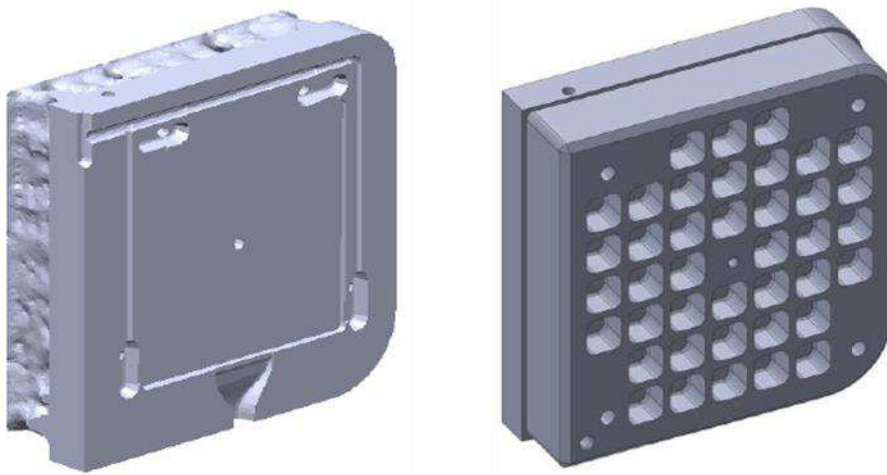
Werkzeugmodelle für die generative (links) und die subtraktive (rechts) Massenreduktion für das Zwillingssplatten-Werkzeug.
